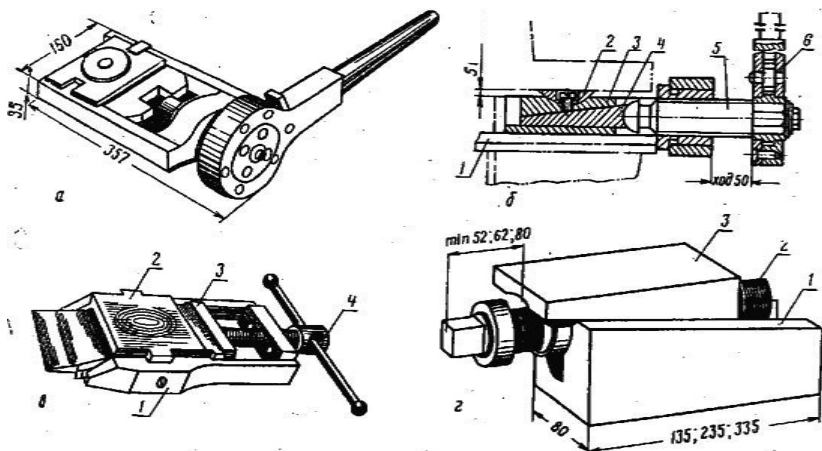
Клинові домкрати для вивірення обладнання та заготовок при розмічанні: а – загальний вигляд; б – схема; 1 – основа; 2 – опорна сферична шайба; 3, 4 – підйомний і рухливий клини; 5 – ходовий гвинт; 6 – тріскачковий ключ; в – домкрат - установка підкладка; 1 – корпус; 2 – підйомна плита; 3 – клин з гайкою; 4 – гвинт з рукояткою; г – клинова регульована підкладка ПР; 1 – нерухомий клин; 2 – ходовий гвинт; 3 – верхній клин з нарізною втулкою
